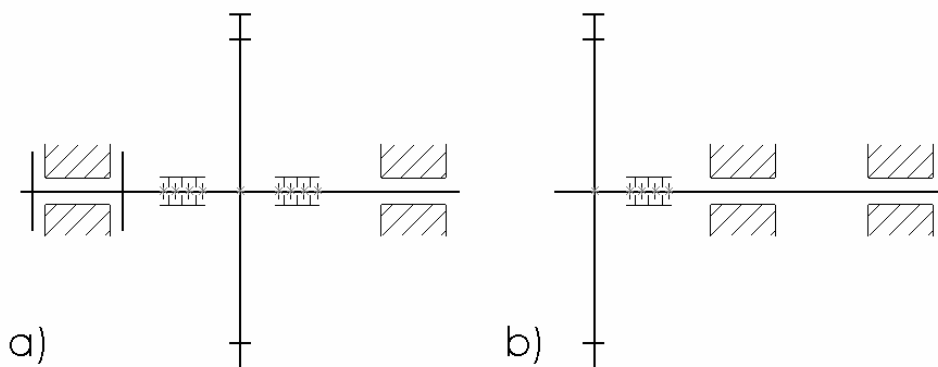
rotorů: a) bubnový typ rotoru (vlevo), b) kolový typ rotoru (vpravo) [3]
